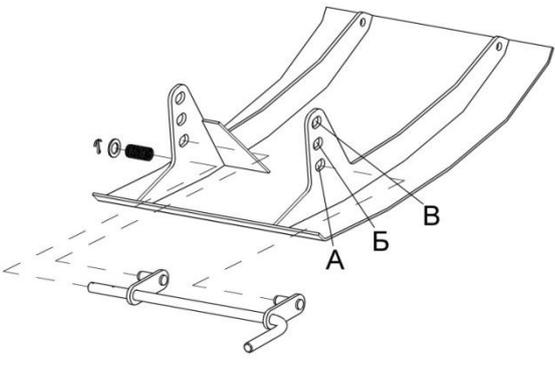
Регулировка механизма продольного копирования жатки
